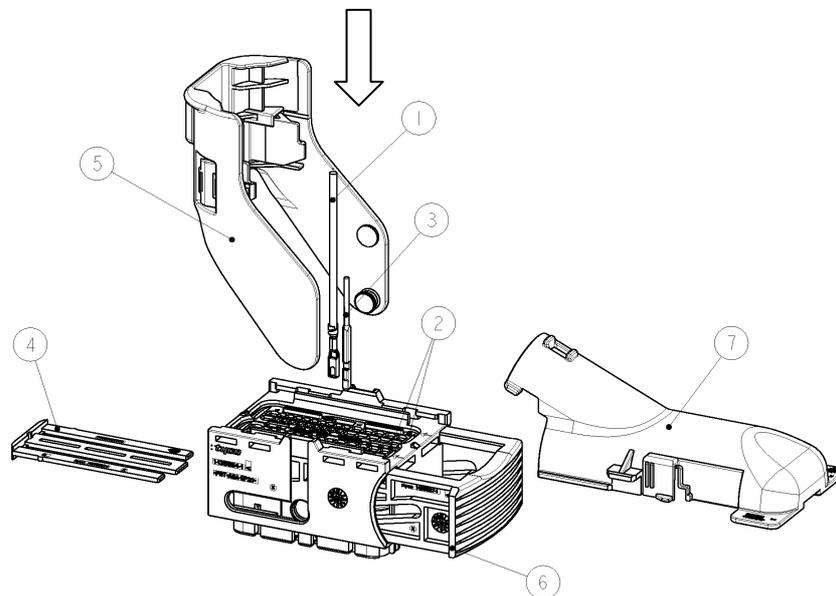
Buchsengehäuse (hier 60 pol.)
